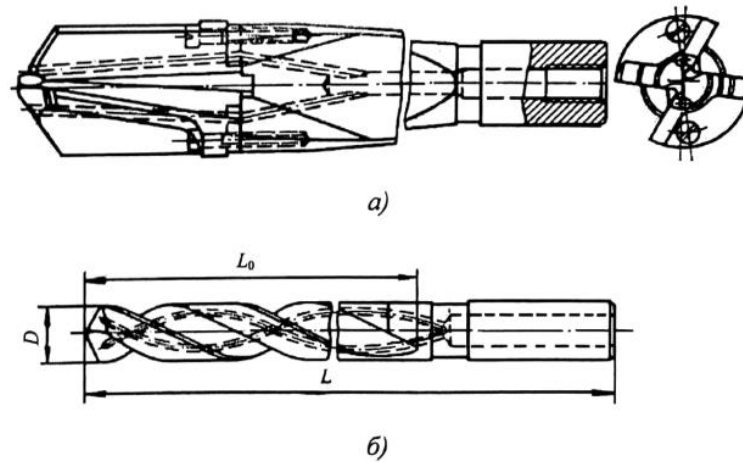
Багатокромкові свердла для глибокого свердління
